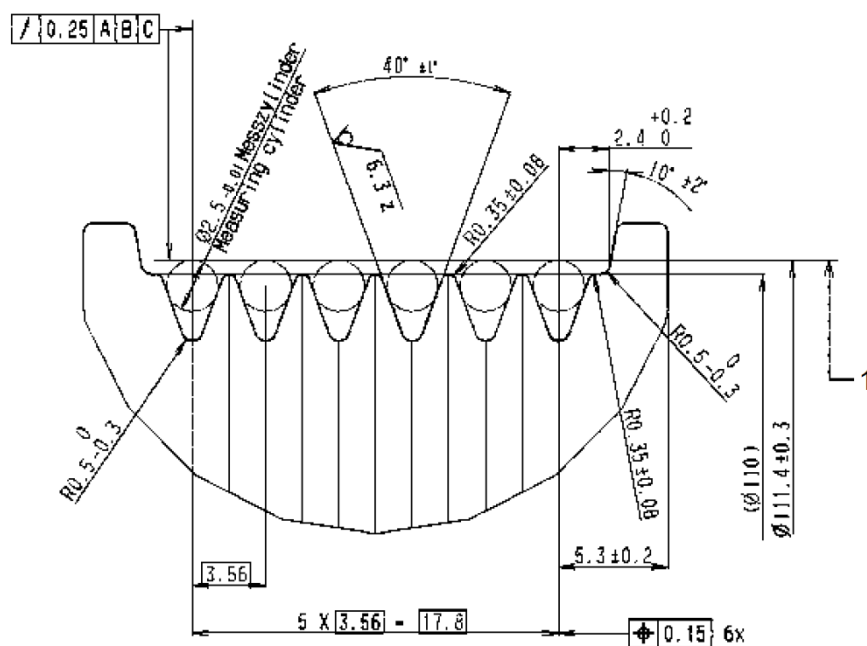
Детальное изображение: U-шків компрессора климатической установки, диаметр шкива – 110 мм
